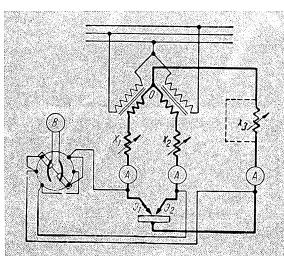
Схема сварочной цепи автомата АДС-1000
